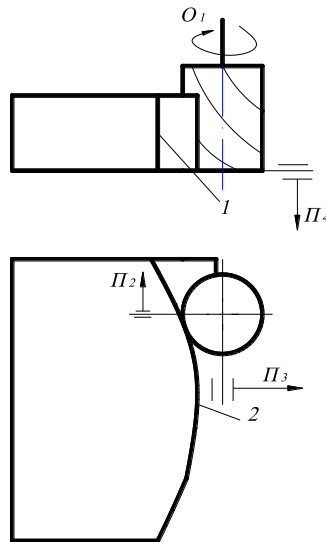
Схема фрезерування криволінійної поверхні кінцевою фрезою
